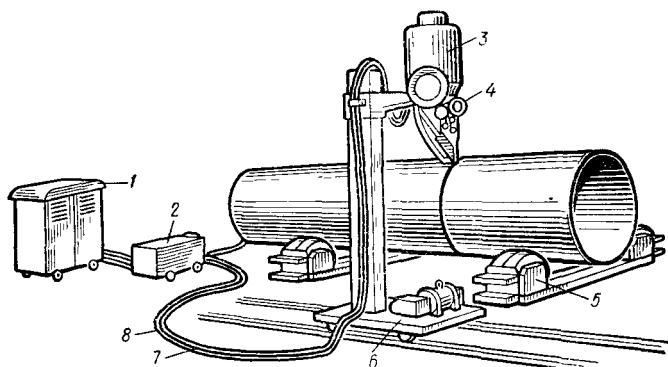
Схема установки для выполнения автоматической сварки под флюсом продольных и кольцевых швов:
